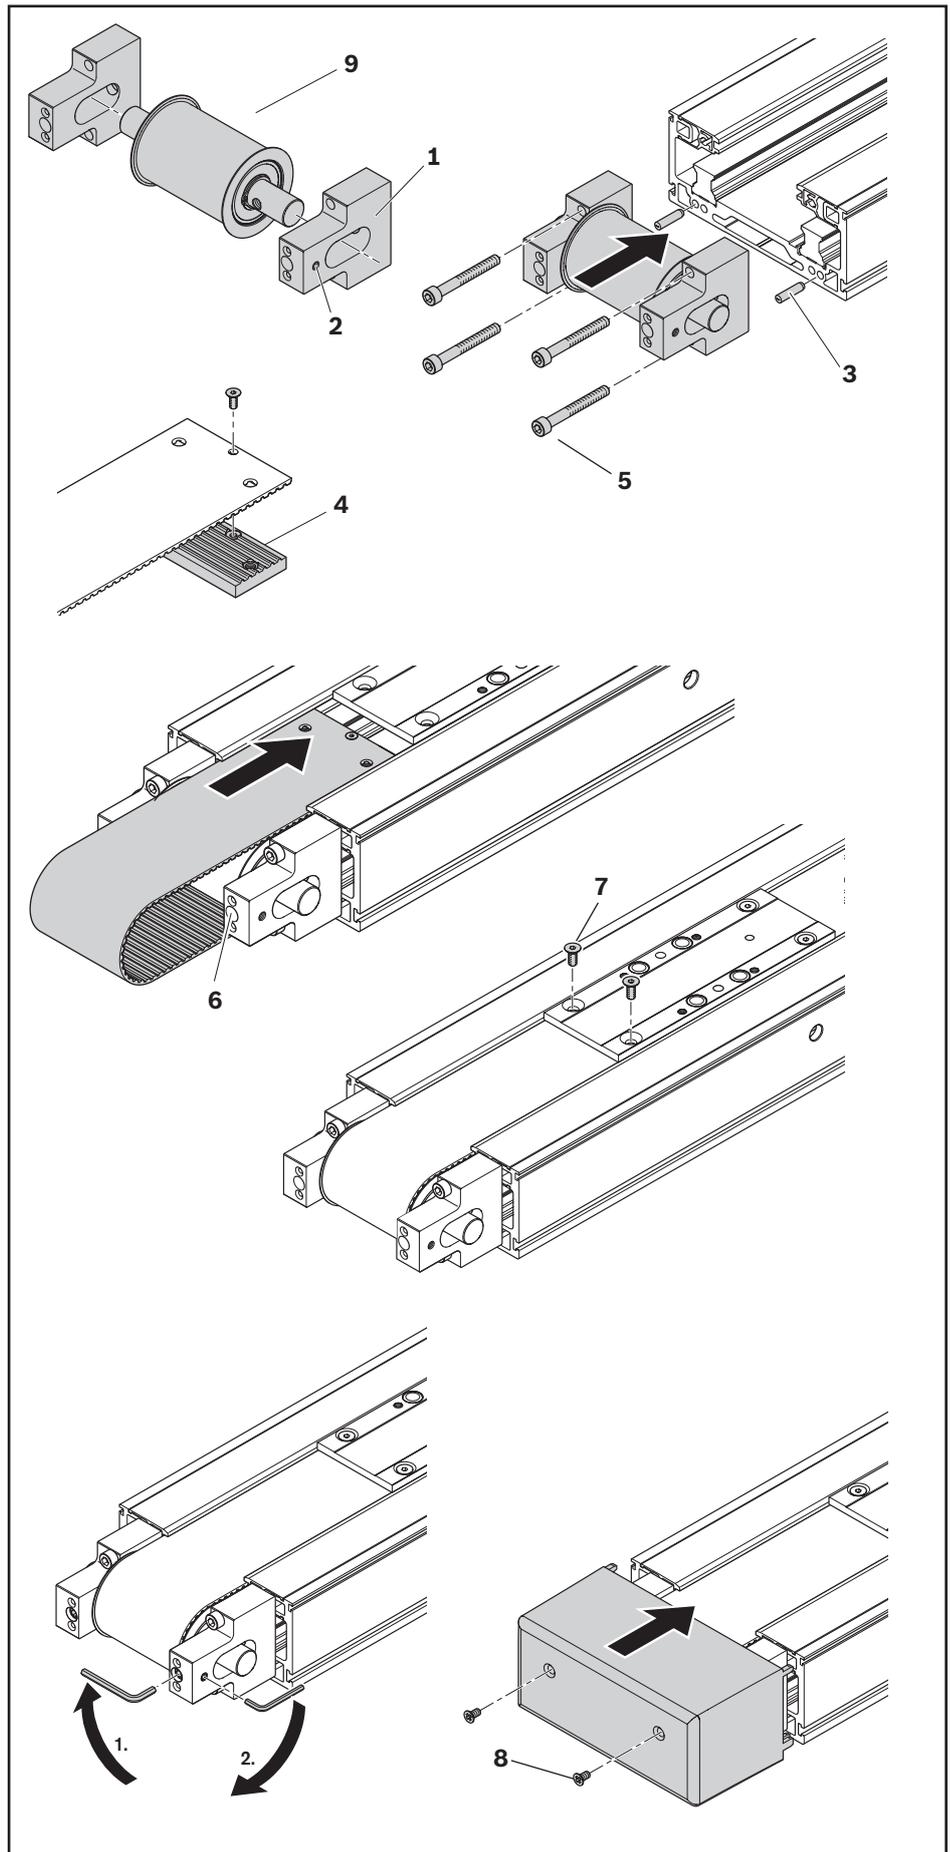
CKR -090, -110, -145, -200, -280 Austausch Endkopf Spannseite
